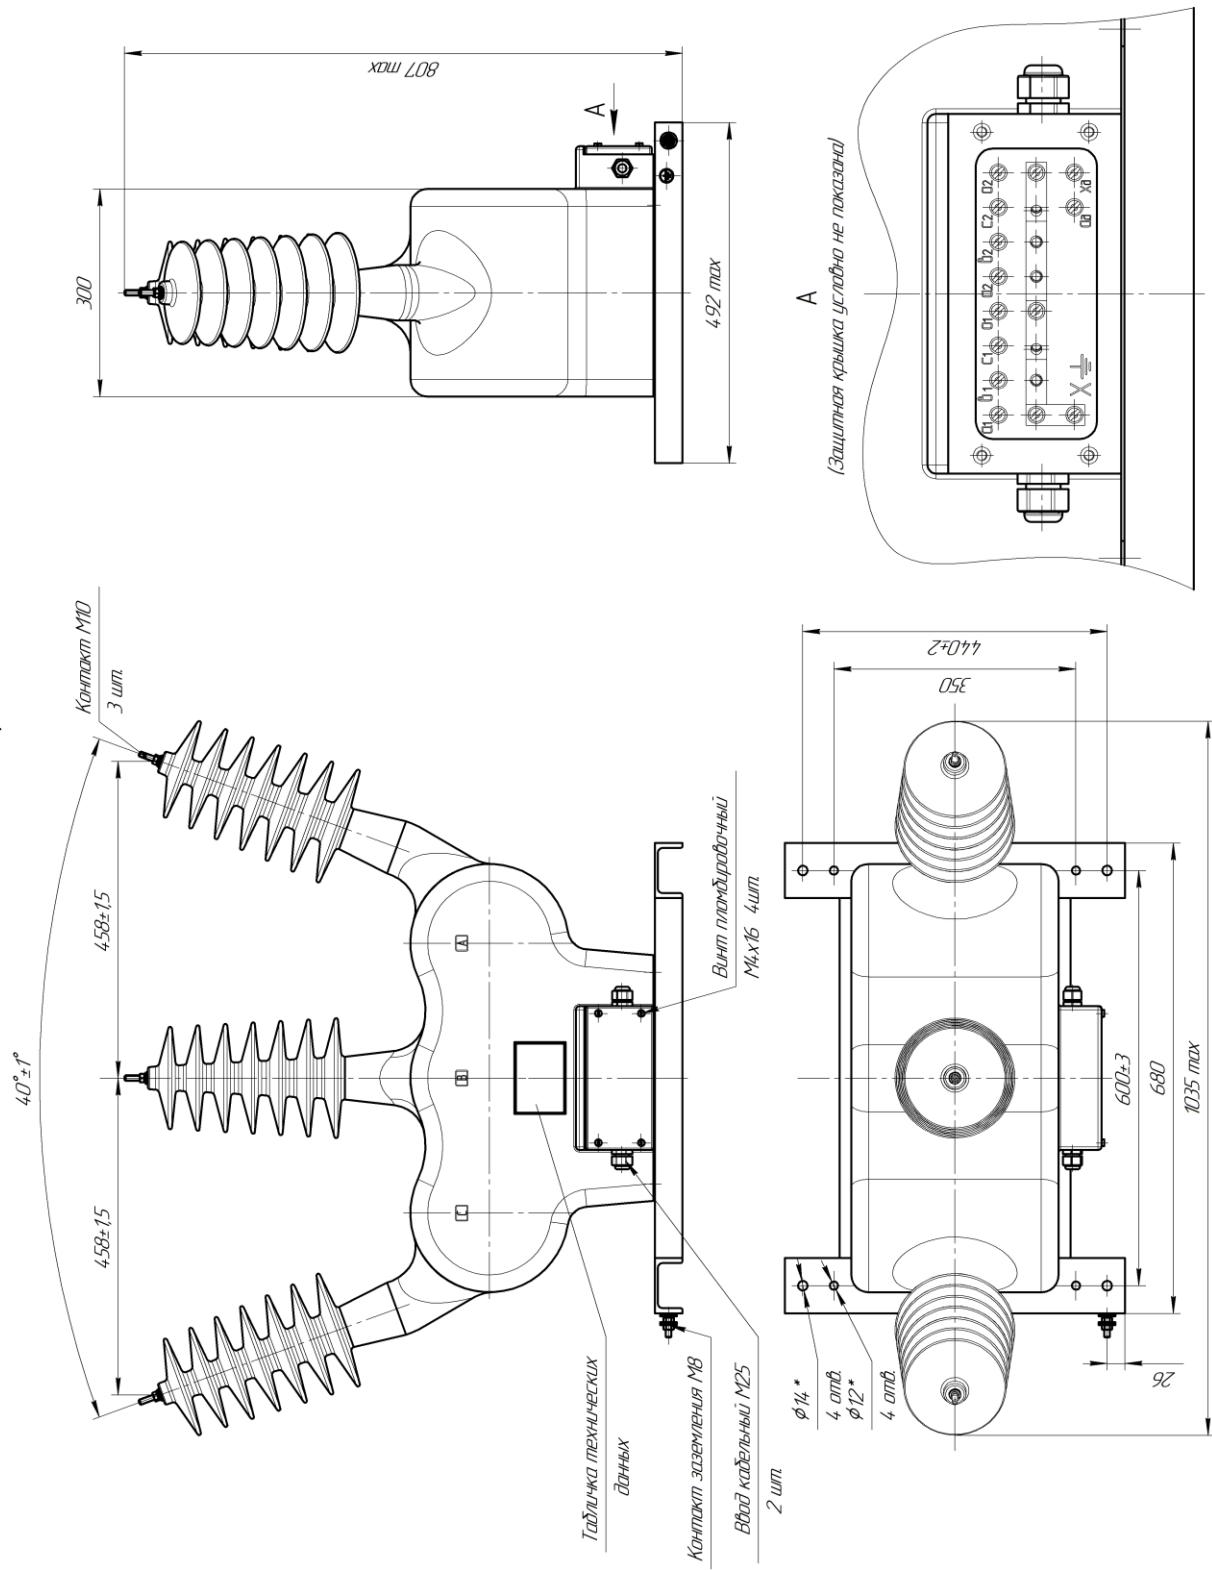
Габаритные, установочные, присоединительные размеры и масса трансформаторов НАЛИ-НТЗ-35-IV
